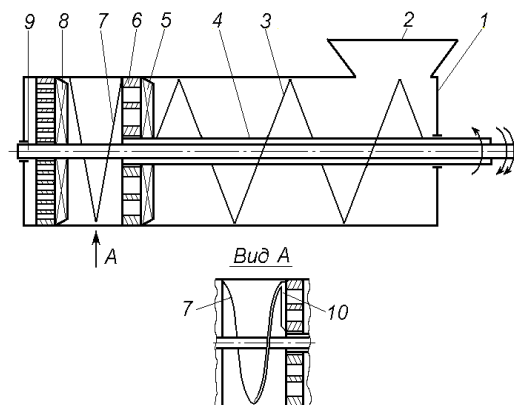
Схема удосконаленого вовчка з додатковим шнеком-активатором: 1 — корпус; 2 — завантажувальна горловина; 3 — основний робочий шнек; 4 — порожнистий приводний вал; 5 — ріжучий ніж; 6 — приймальна решітка; 7 — шнек-активатор; 8 — подрібнювальний пристрій; 9 — приводний вал; 10 — твірна кромка шнека 7.
